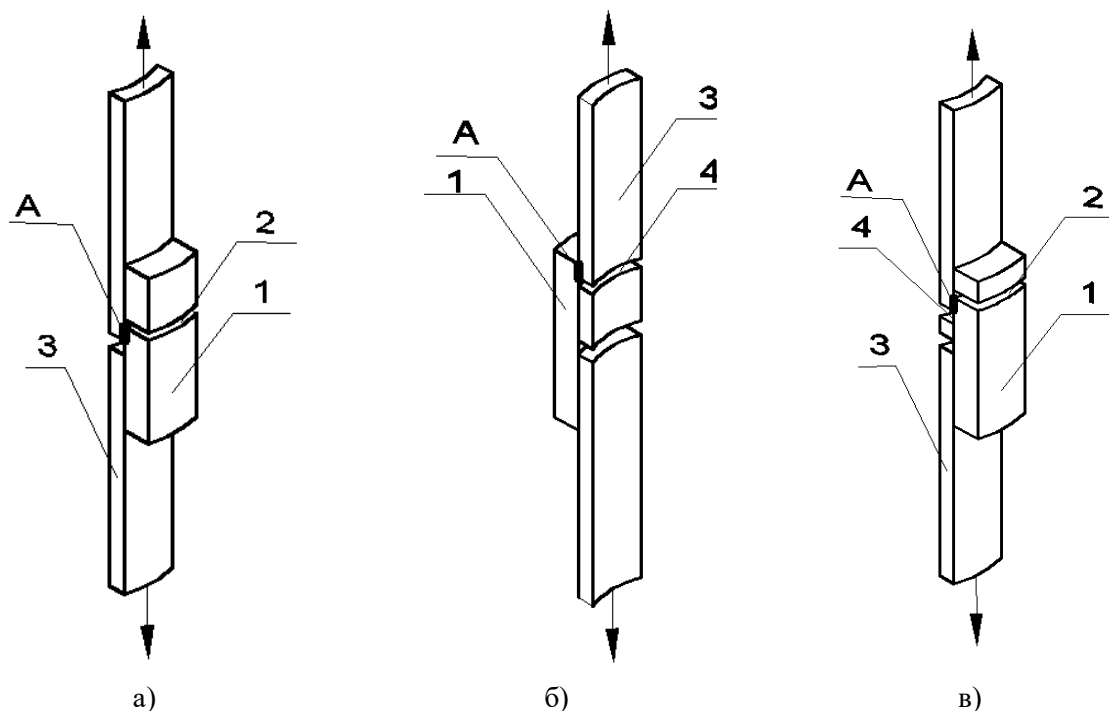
Схема расположения испытуемых областей сварки в раструбном сварном соединении полипропиленовых труб
